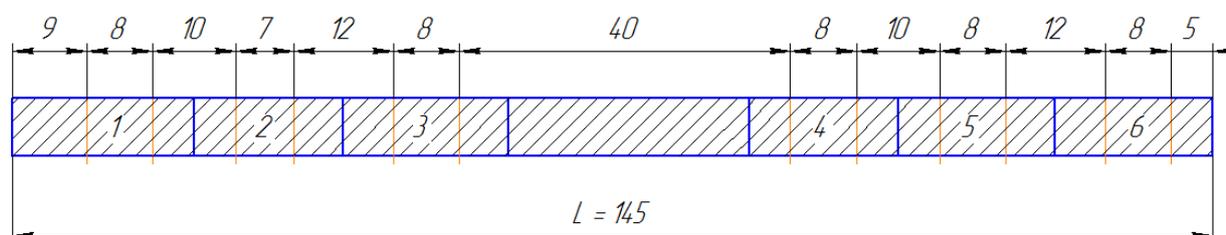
Схема вырезки опытных образцов с размерами (L – ширина лемеха)
